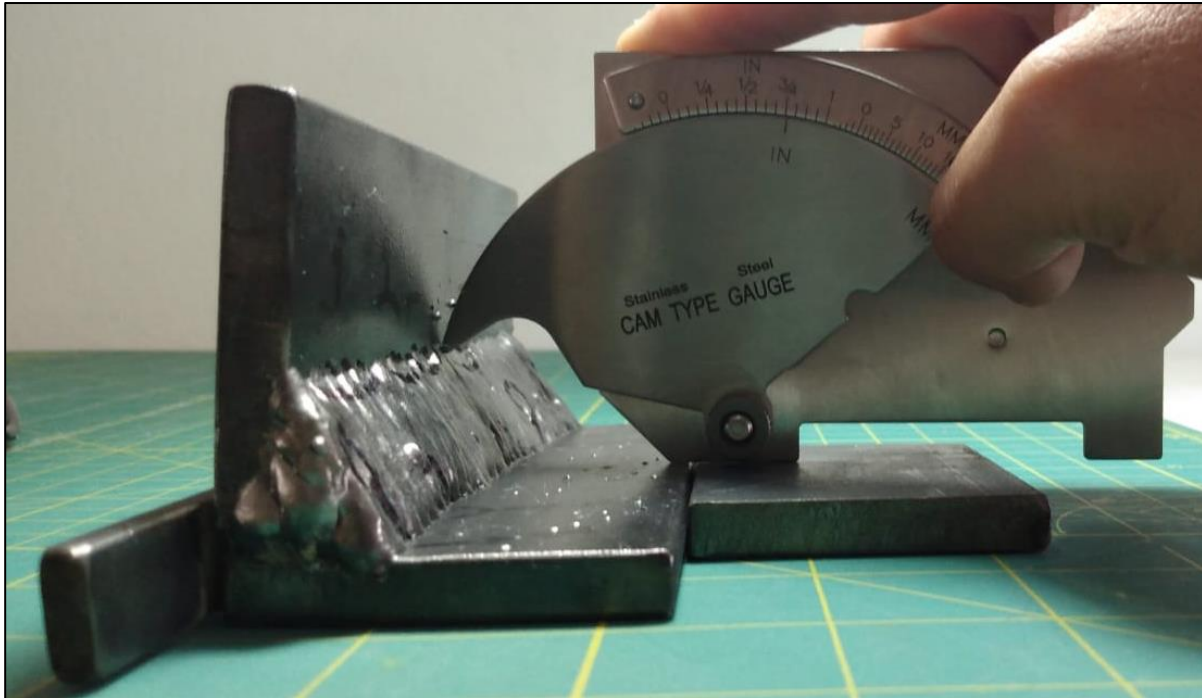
Medición De La Altura De La Soldadura De Filete [64].
